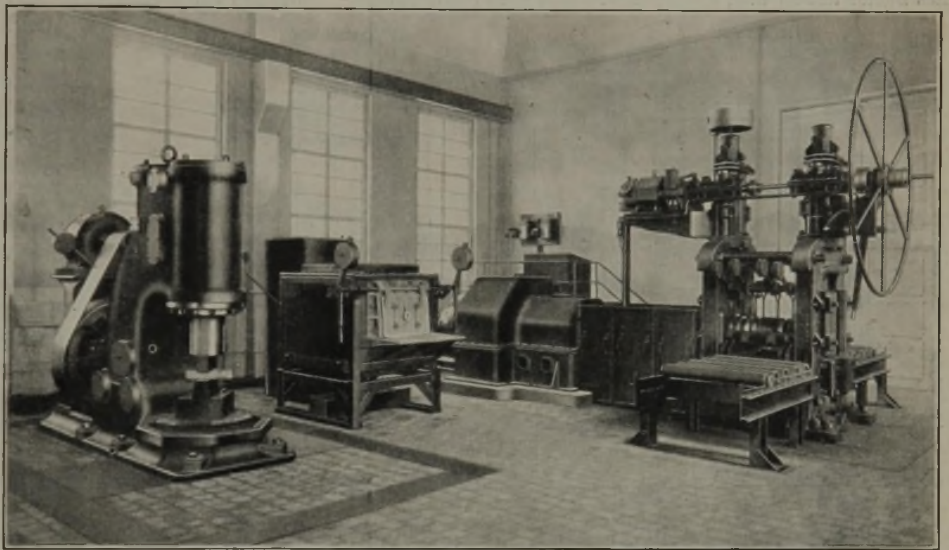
Teilansicht der metallurgischen Halle. Versuchswalzwerk und großer Lufthammer.
